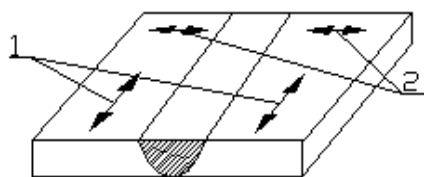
Продольные (1) и поперечные (2) напряжения в сварном соединении [7]
